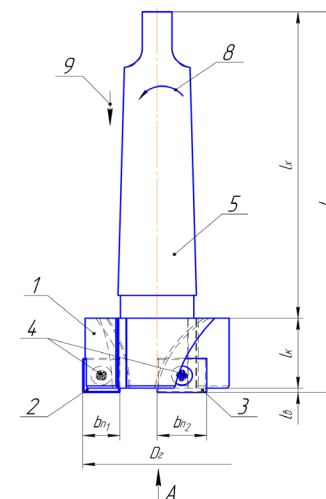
Сборная резцовая головка с твёрдосплавными пластинами разной ширины
